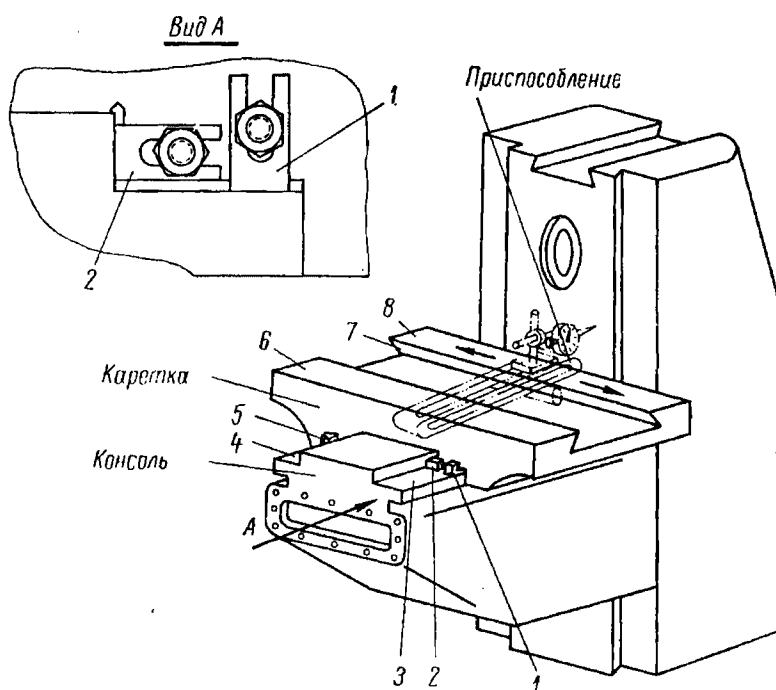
Установка каретки на консоли для восстановления нижних направляющих
